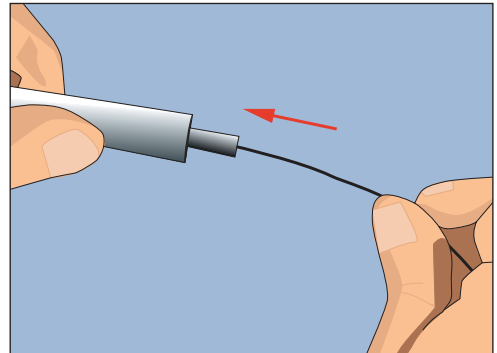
Привязываем к приспособлению для гибки бечевку или провод
